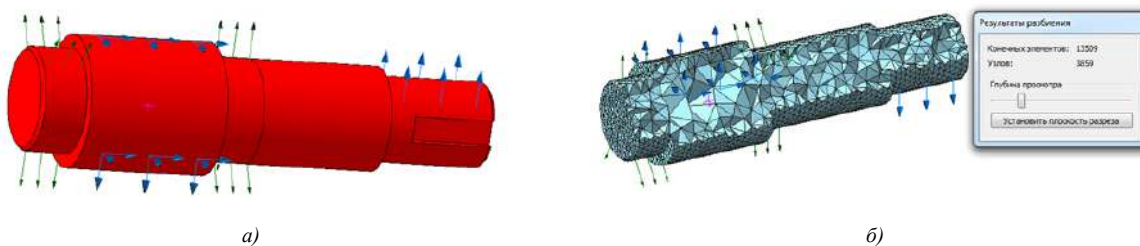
Схема нагружения вала и КЭ-сетка
